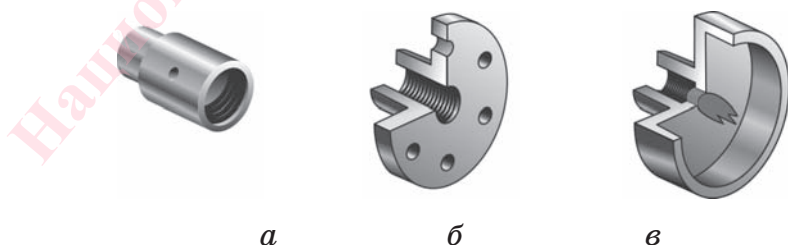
Приспособления для закрепления заготовок при точении: а — патрон; б — планшайба; в — трезубец
